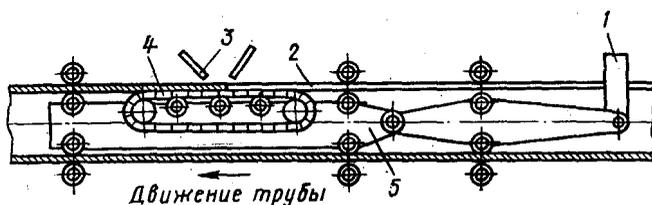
Схема сварки наружного шва трубы на стане проходного типа
